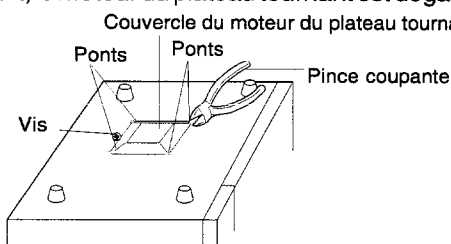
(a). Dépose du couvercle du moteur du plateau tournant
